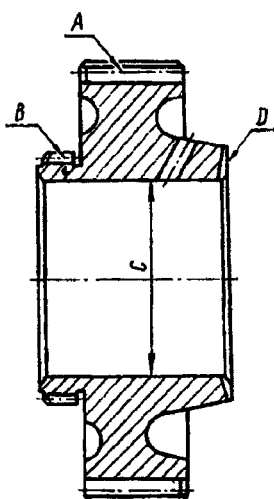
Колесо зубчатое повышающей передачи дифференциала
